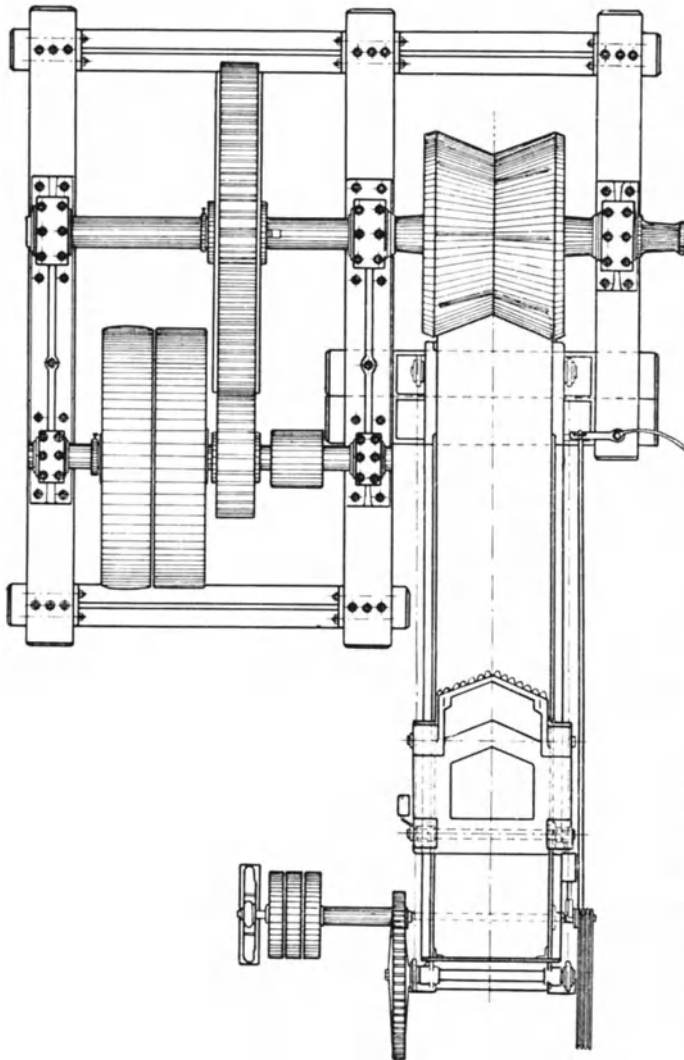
Trommelschneidemaschine (großer Typ) mit mechanischer Zuführung des Holzes
